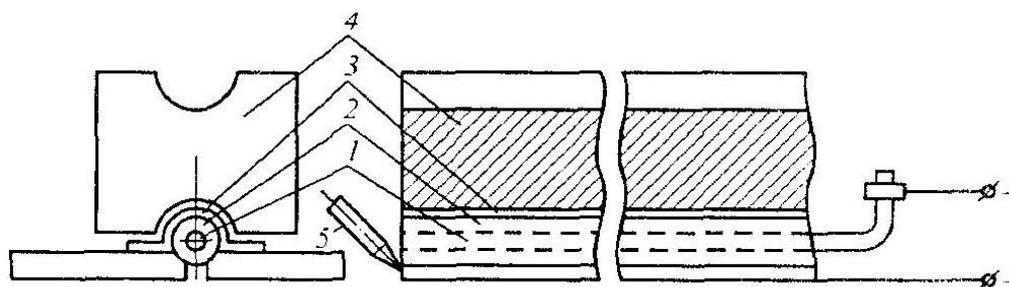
Схема сварки лежачим электродом:
